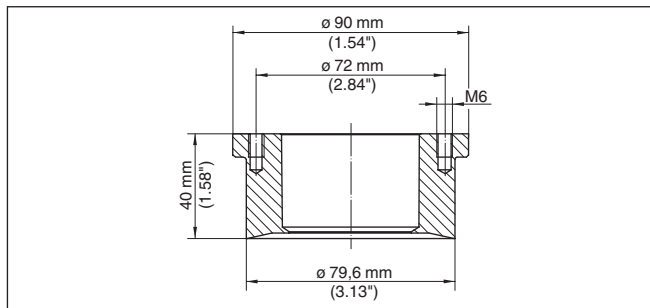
Dimensioni tronchetto a saldare attacco asettico DN 32 con flangia di serraggio
